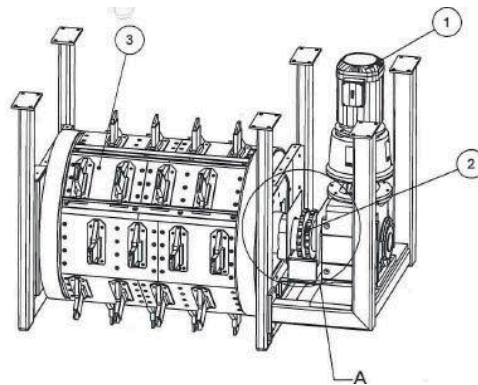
Rotor dentado. 1-Motor 15kW; 2-Acoplamiento rotor; 3-Dientes de rotor
